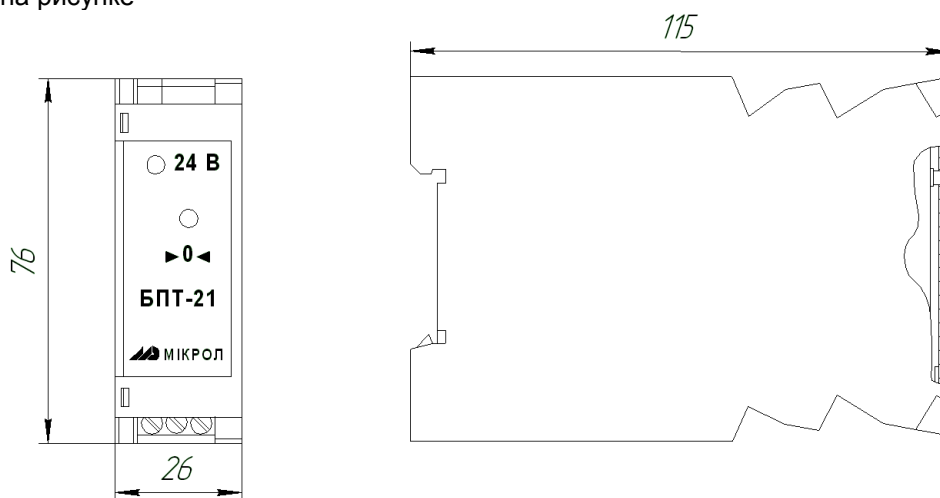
Внешний вид и габаритные размеры БПТ-21
